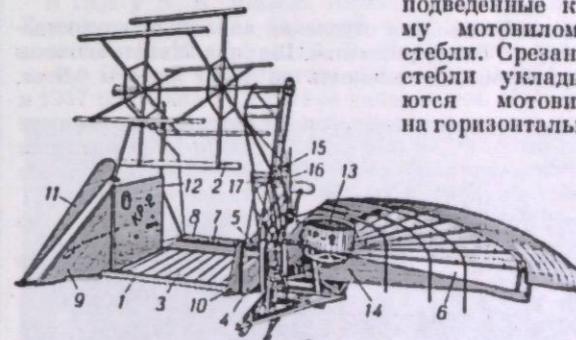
Коноплерасстилочная машина КР-2: 1 — режущий аппарат; 2 — мотовило; 3 — горизонтальный транспортер; 4 — наклонный элеватор; 5 — шит элеватора; 6 — расстилочный аппарат; 7 — цепочно-пальчатый транспортер; 8 — дополнительная платформа; 9 — полевой делитель; 10 — внутренний делитель; 11 — шит полевого делителя; 12 — полевая стенка; 13 — шит расстилочного аппарата; 14 — барабан; 15 — рычаг механизма наклона машины; 16 — рычаг механизма перемещения мотовила; 17 — стойка мотовила.
